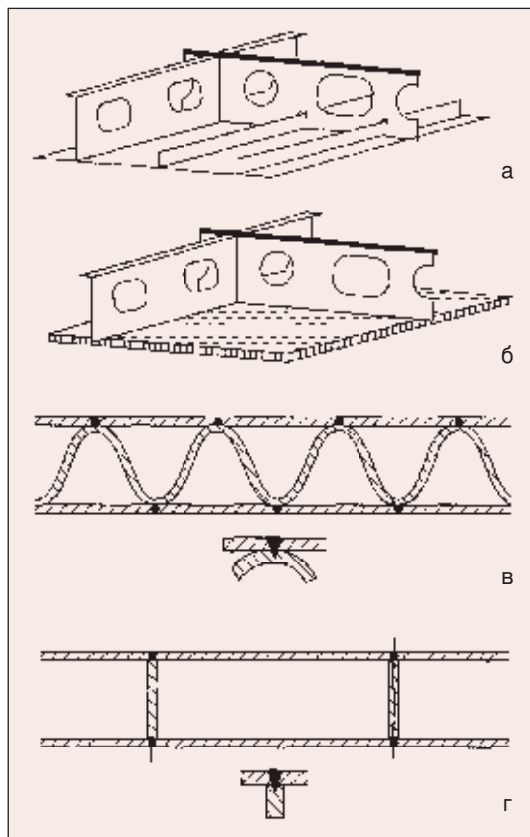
Варианты изготовления судовых панелей: а — конструкция обычного типа; б — конструкция типа «сэндвич», выполненная лазерной сваркой; в — конструкция типа Lascor; г — конструкция типа Meyer-Werft
